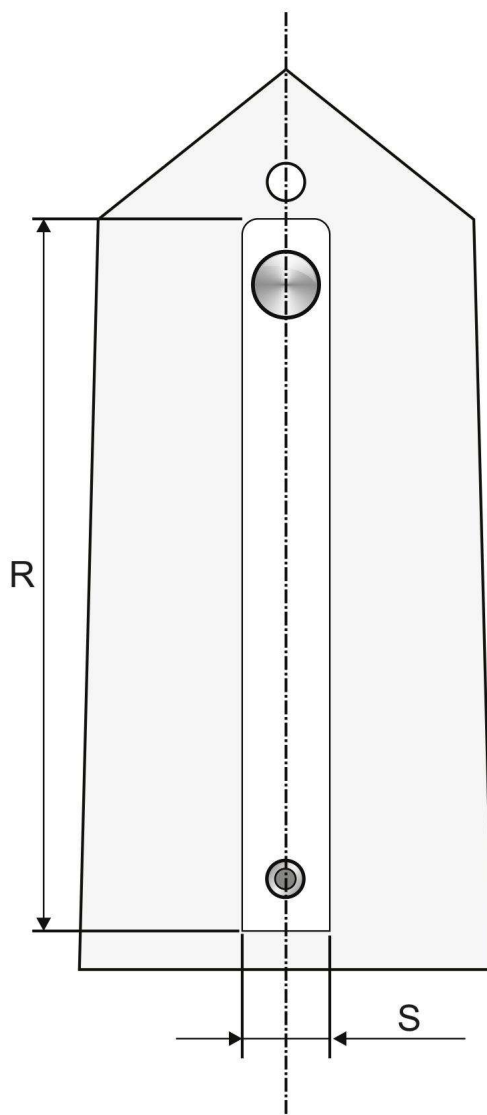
Platinas montadas e respectivos PN - Oficiais-generais Aviadores
